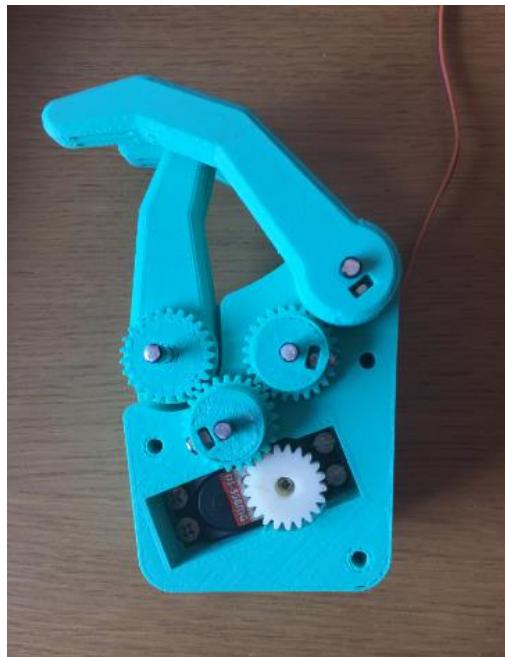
Sistema de engranajes con la pinza cerrada
